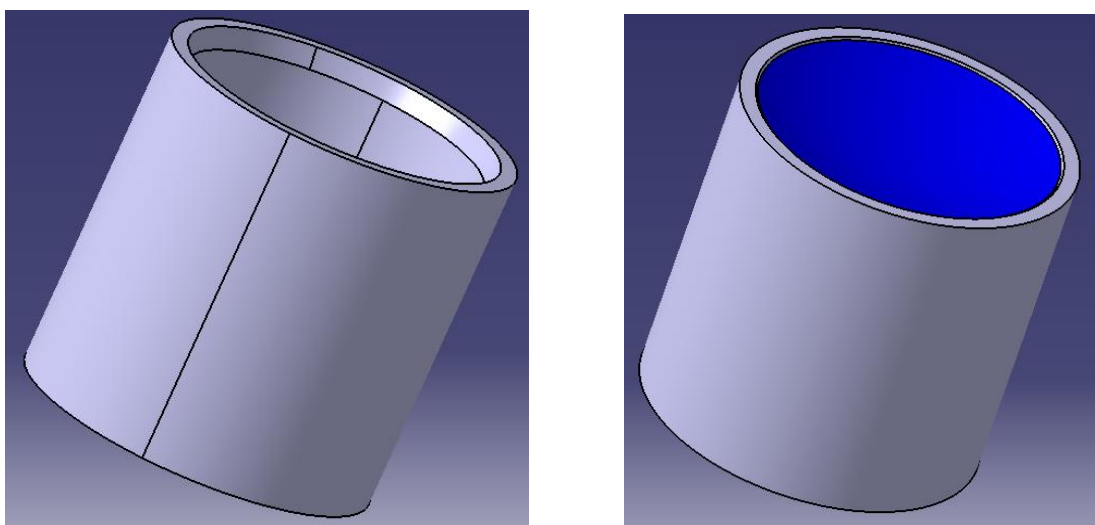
Diseño 3D del soporte cónico (izquierda). Soporte cónico con transductor posicionado (derecha)
